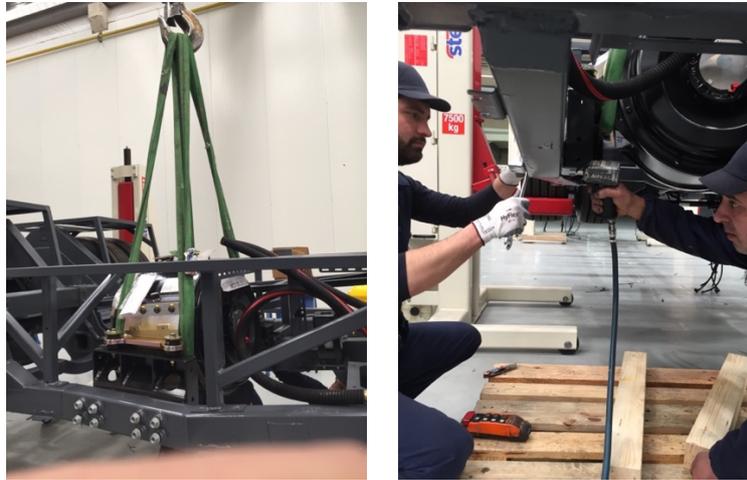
Montagem do motor no chassi já com a melhoria realizada.
